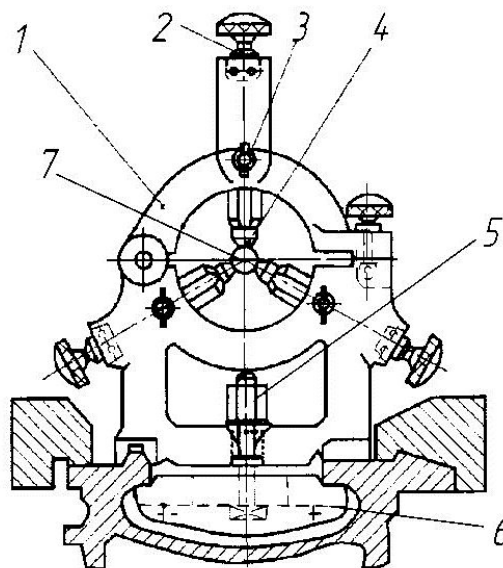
Неподвижный люнет: 1 — откидная часть (крышка); 2 — винт; 3 — стопор; 4 — кулачок; 5 — гайка зажима башмака; 6 — башмак; 7 — заготовка
